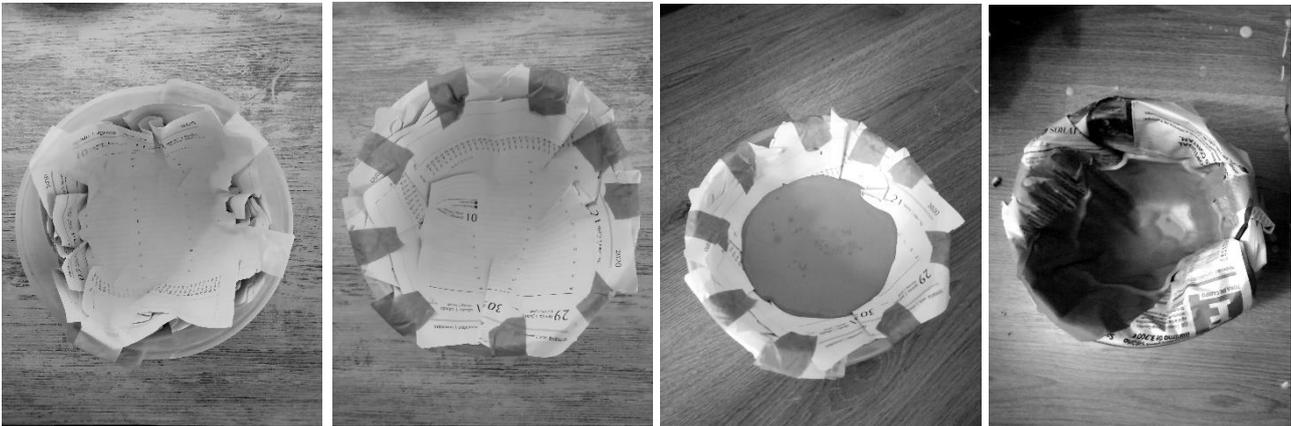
Molde de papel – Fixação da última camada – Enchimento – Peça após esvaziar molde
